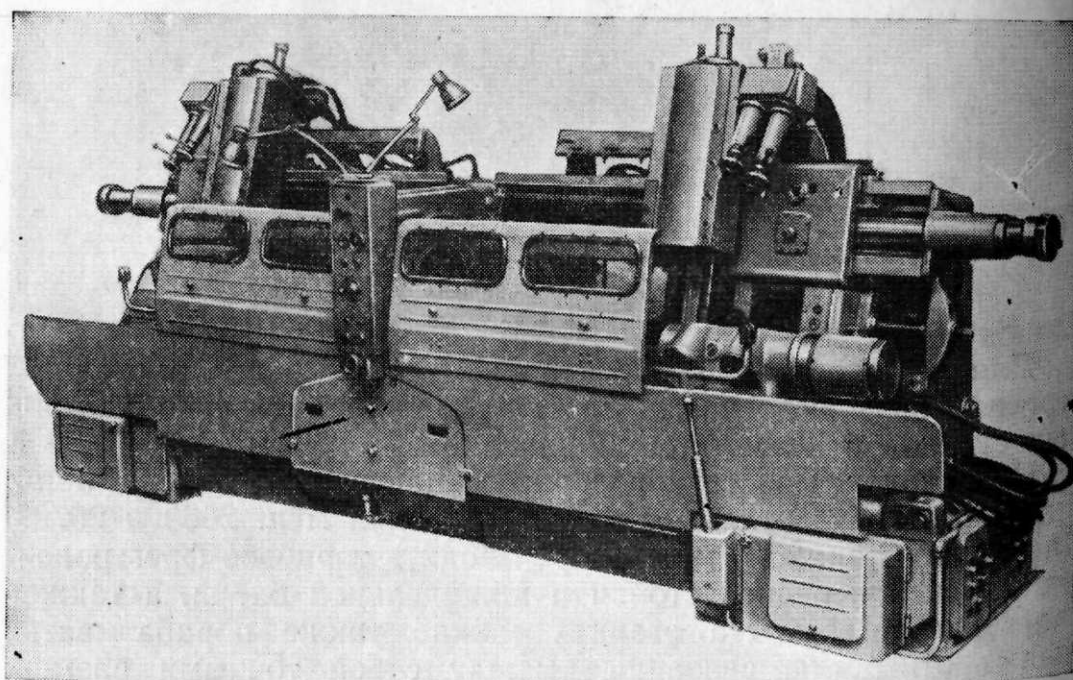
Универсальный токарно-копировальный полуавтомат мод. 1722.
